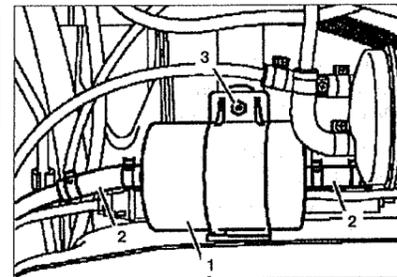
Топливный фильтр двигателей 111.948 и 104.900:
